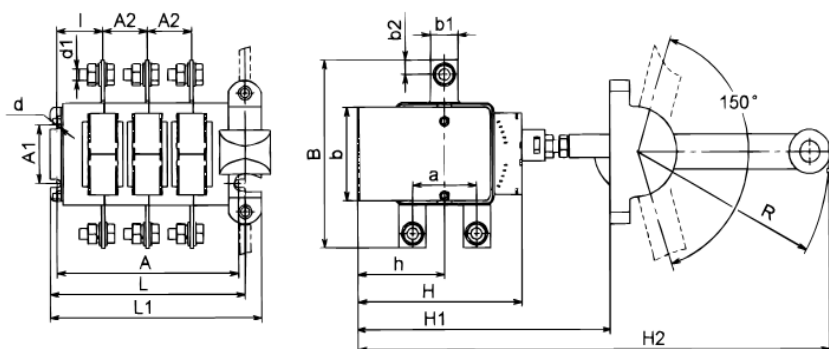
Б Выключатель-разъединитель на два направления трехполюсный с передней смещенной рукояткой
